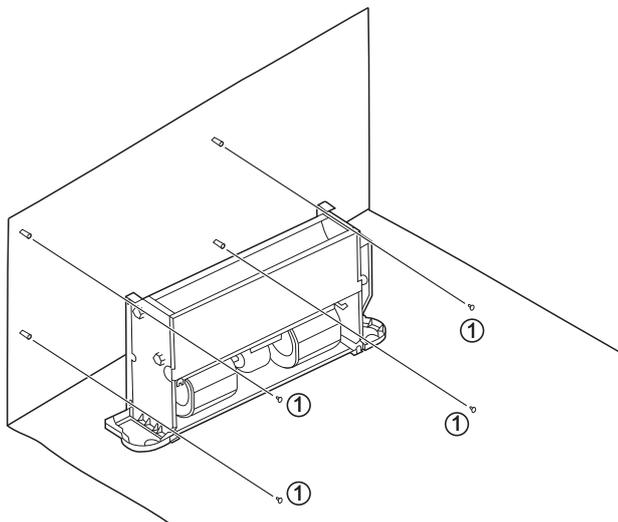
Ansicht zur Befestigung des Gehäuses
